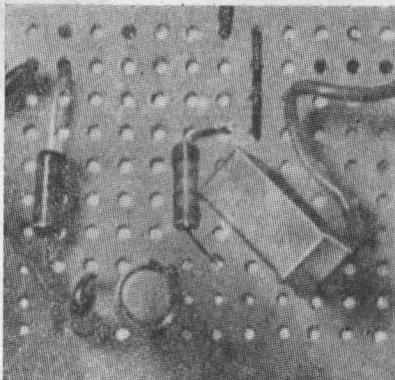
FOTO I — Plaqueta de circuito impresso universal já com os componentes do provador. Não é necessário realizar-se interrupções nos filetes de cobre.
